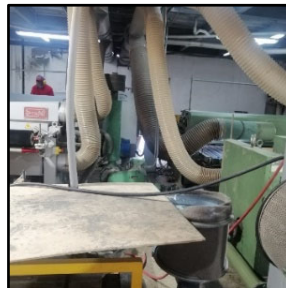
Turbina 1 extractora de polvo de la máquina ALETTI
